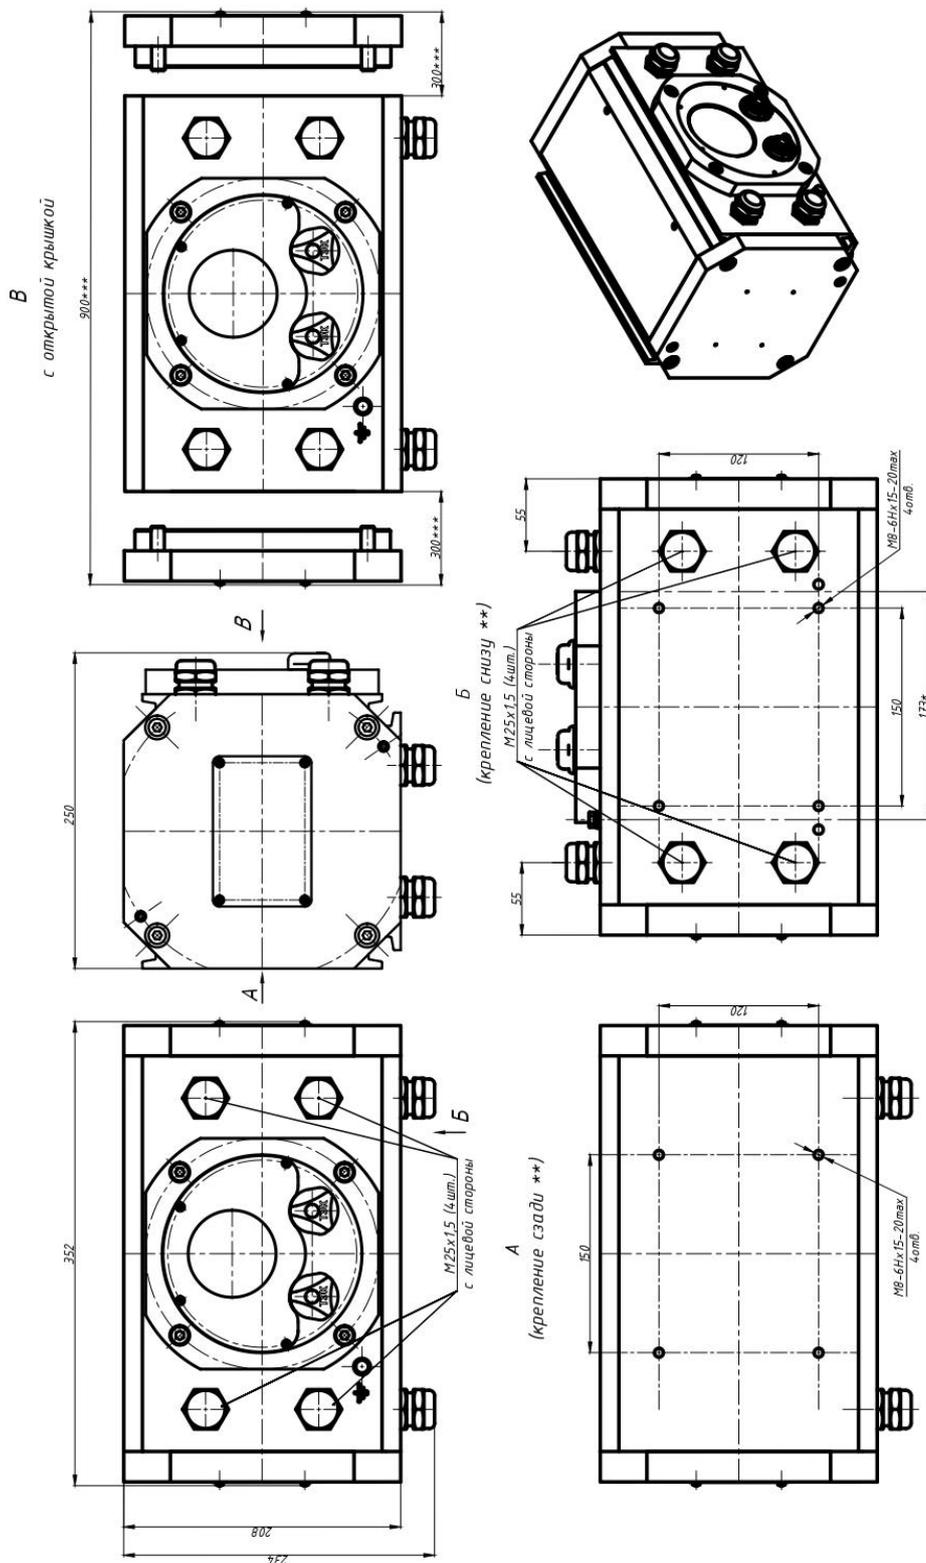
Внешний вид и габаритные размеры БДУ-V
